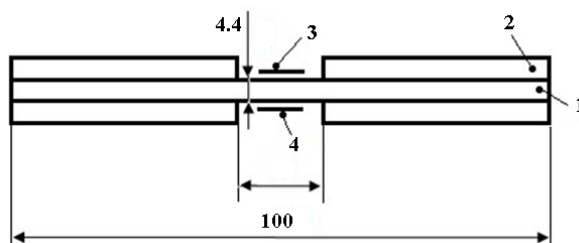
Dimensiunile epruvetei GFRP, conform ASTM 695
